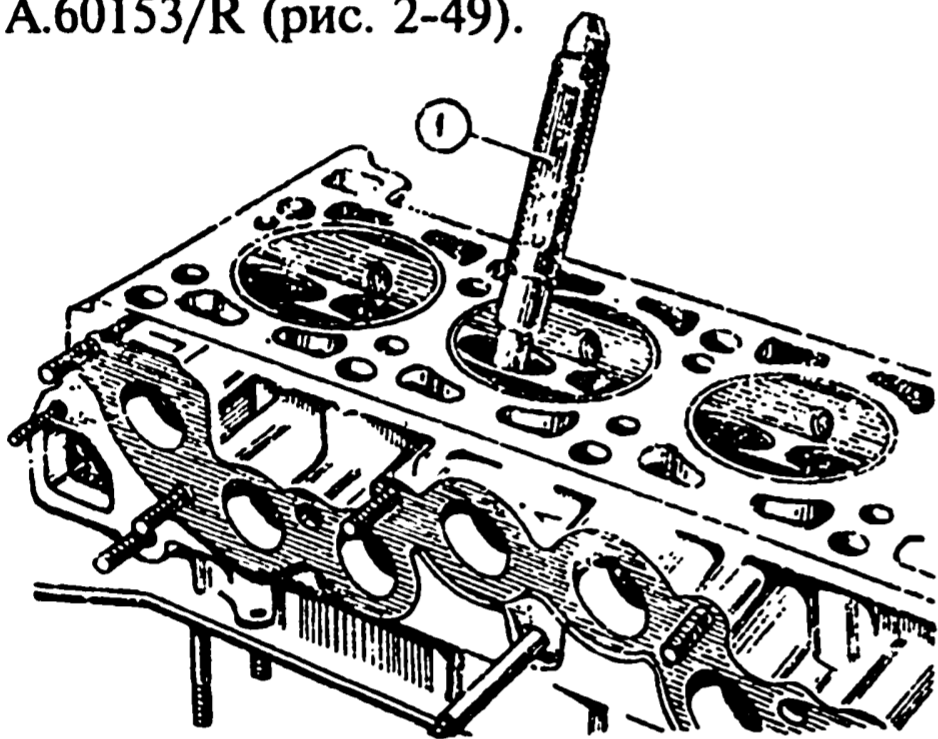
Выпрессовка направляющих втулок: 1 - оправка А.60153/R
